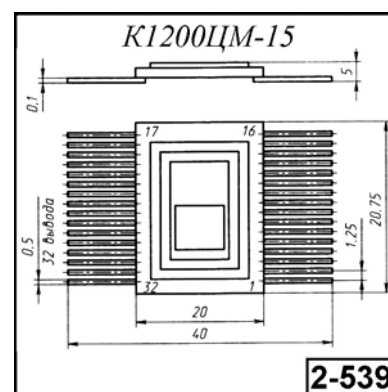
Внешний вид и габаритные размеры К1200ЦМ15
